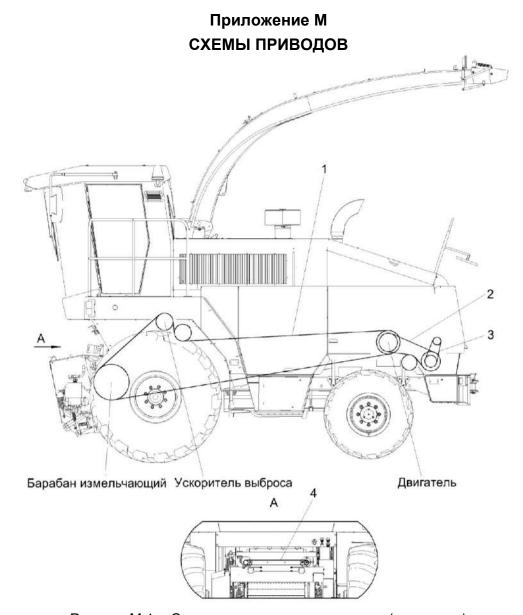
Схема приводов измельчителя (вид слева)
